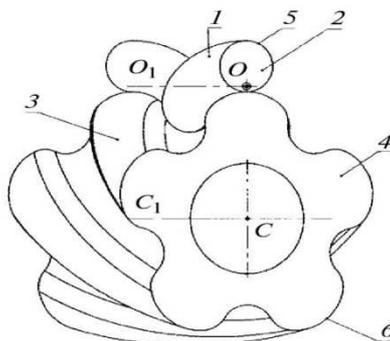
Поверхности зубьев колеса идеального зацепления [20]
